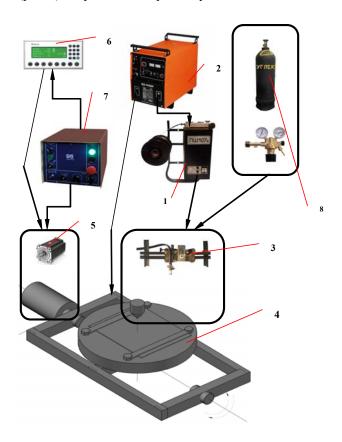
Установка для наплавки в среде углекислого газа с колебаниями сварочной ванны: 1 — полуавтомат сварочный;2 — источник питания сварочной дуги; 3 — сварочная горелка и механизм её перемещения; 4 — подвижный стол с закреплённой деталью; 5 — шаговый двигатель; 6 — пульт управления шаговым двигателем; 7 — блок управления шаговым двигателем; 8 — баллон с углекислым газом
